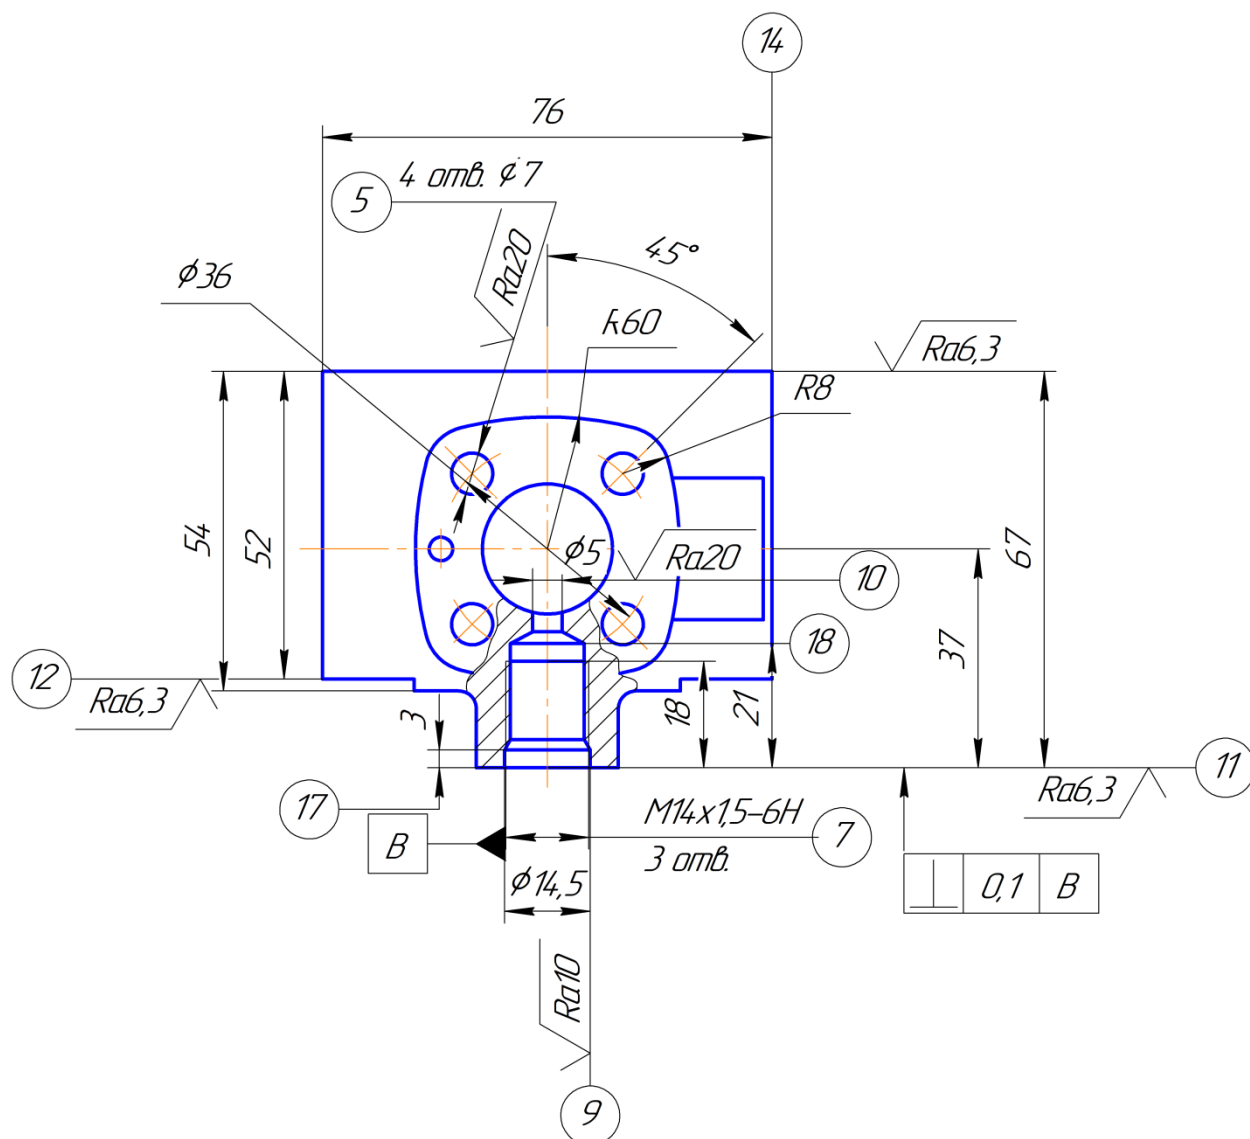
Вид Б по чертежу. Нумерация поверхностей детали.
